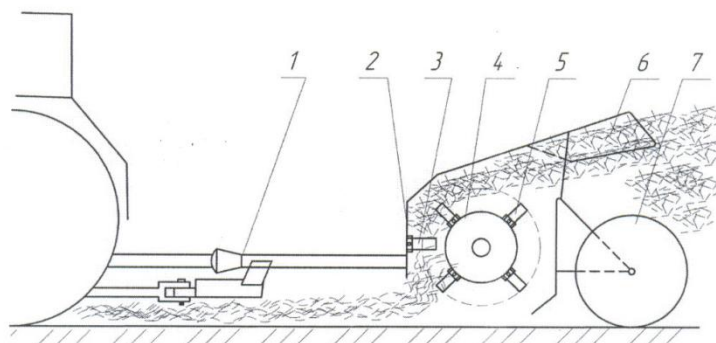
Технологическая схема 1 прицепного: 1 - карданный вал; 2 - корпус; 3 - противорезы; 4 - роторный подбирающий аппарат (измельчающий барабан); 5 - нож измельчающего барабана; 6 - разбрасыватель; 7 - колесо
